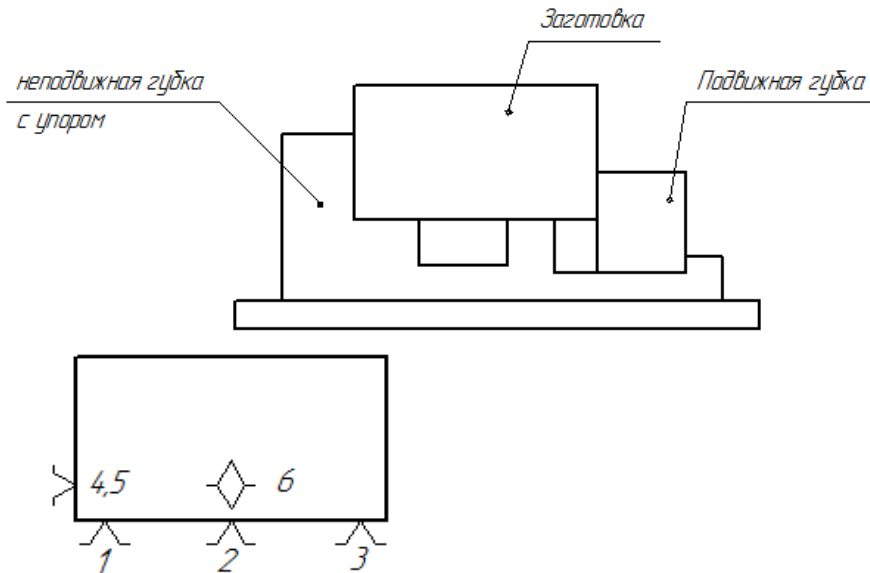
Установка й схема базування заготовки в лещатах [30].
